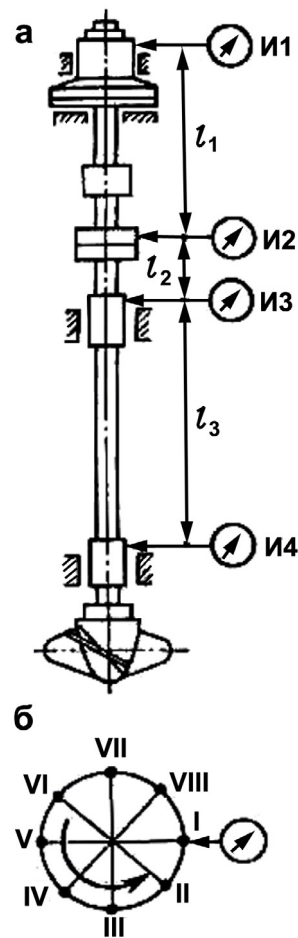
Выверка излома вала насосного агрегата по индикаторам:
